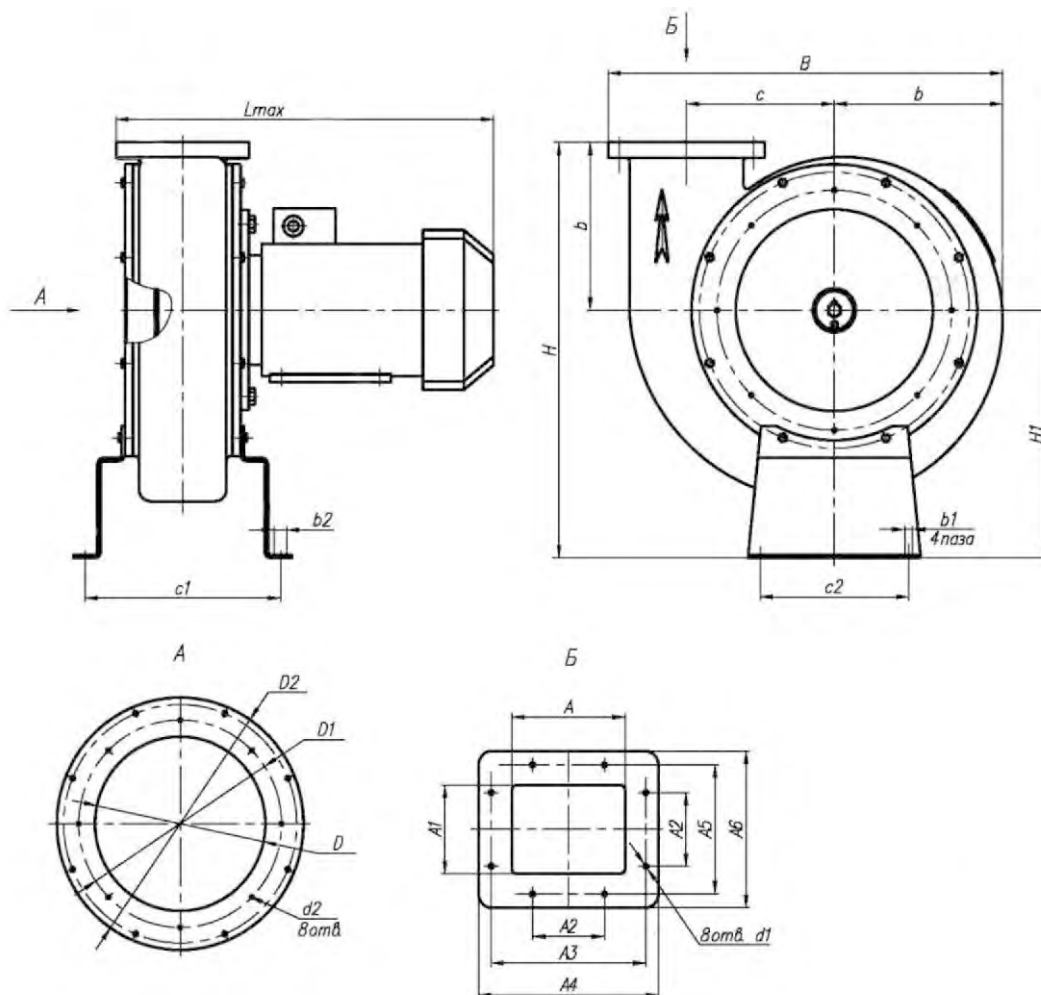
Габаритные и присоединительные размеры 12-26 СЧ (с улитой из чугуна).
